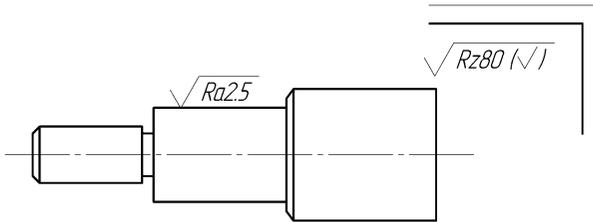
Пример обозначения шероховатости одинаковой для части поверхностей детали
